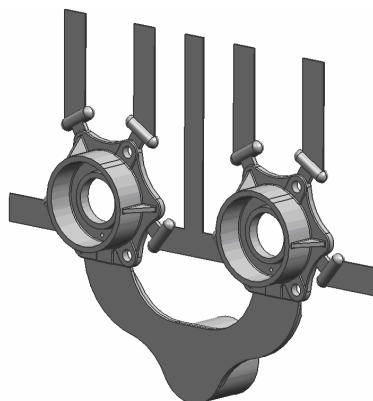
трехмерная модель отливки «Корпус 007»
